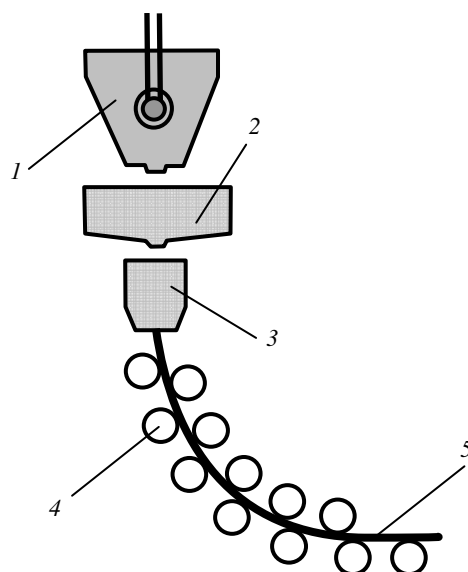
Радиальная МНЛЗ: 1 — стелеразливочный ковш; 2 — промежуточный ковш; 3 — кристаллизатор; 4 — рольганг; 5 — непрерывно-литой слиток
